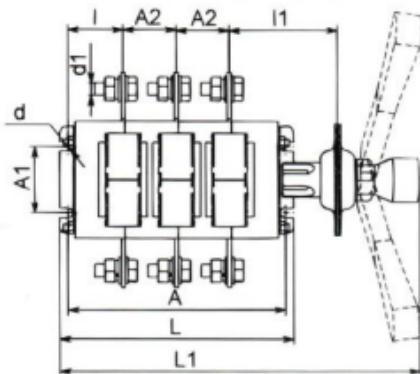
Выключатель-разъединитель на два направления трехполюсный с боковой смещенной рукояткой
